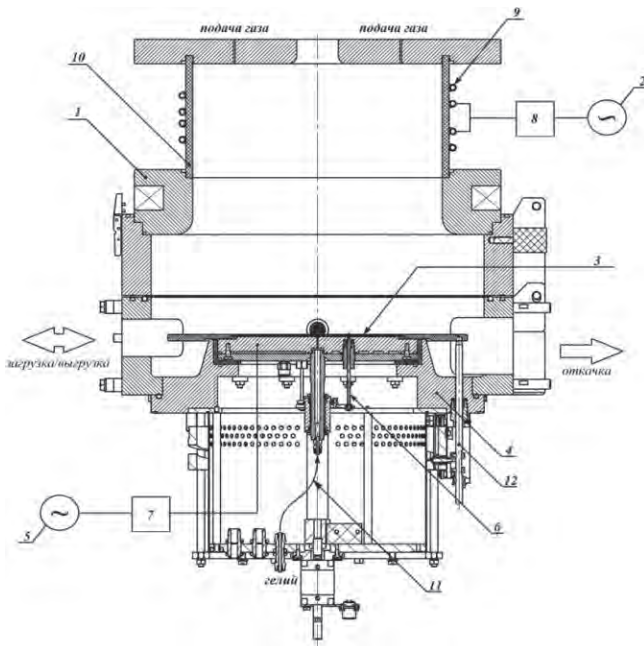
Конструкция реактора установки для Bosch-процесса (1 — источник плазмы; 2 — ВЧ-генератор; 3 — рабочая пластина; 4 — подложкодержатель; 5 — ВЧ-генератор; 6 — механизм вертикального перемещения; 7 — устройство автоматического согласования; 8 — устройство согласования; 9 — индуктор; 10 — кварцевая колба; 11 — гелиевое охлаждение; 12 — механический прижим)
